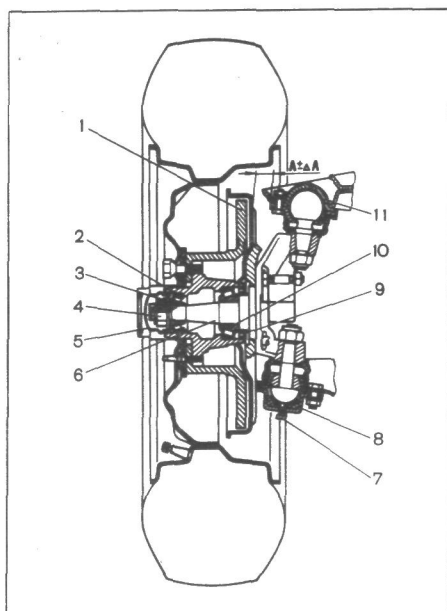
Переднее колесо: 1 — тормозной диск; 2 — ступица; 3 — наружный роликовый подшипник; 4 — гайка крепления ступицы; 5 — колпачок; 6 — поворотный кулак; 7 — пробка; 8 — шаровая опора нижнего рычага; 9 — сальник; 10 — внутренний роликовый подшипник; 11 — шаровая опора верхнего рычага
